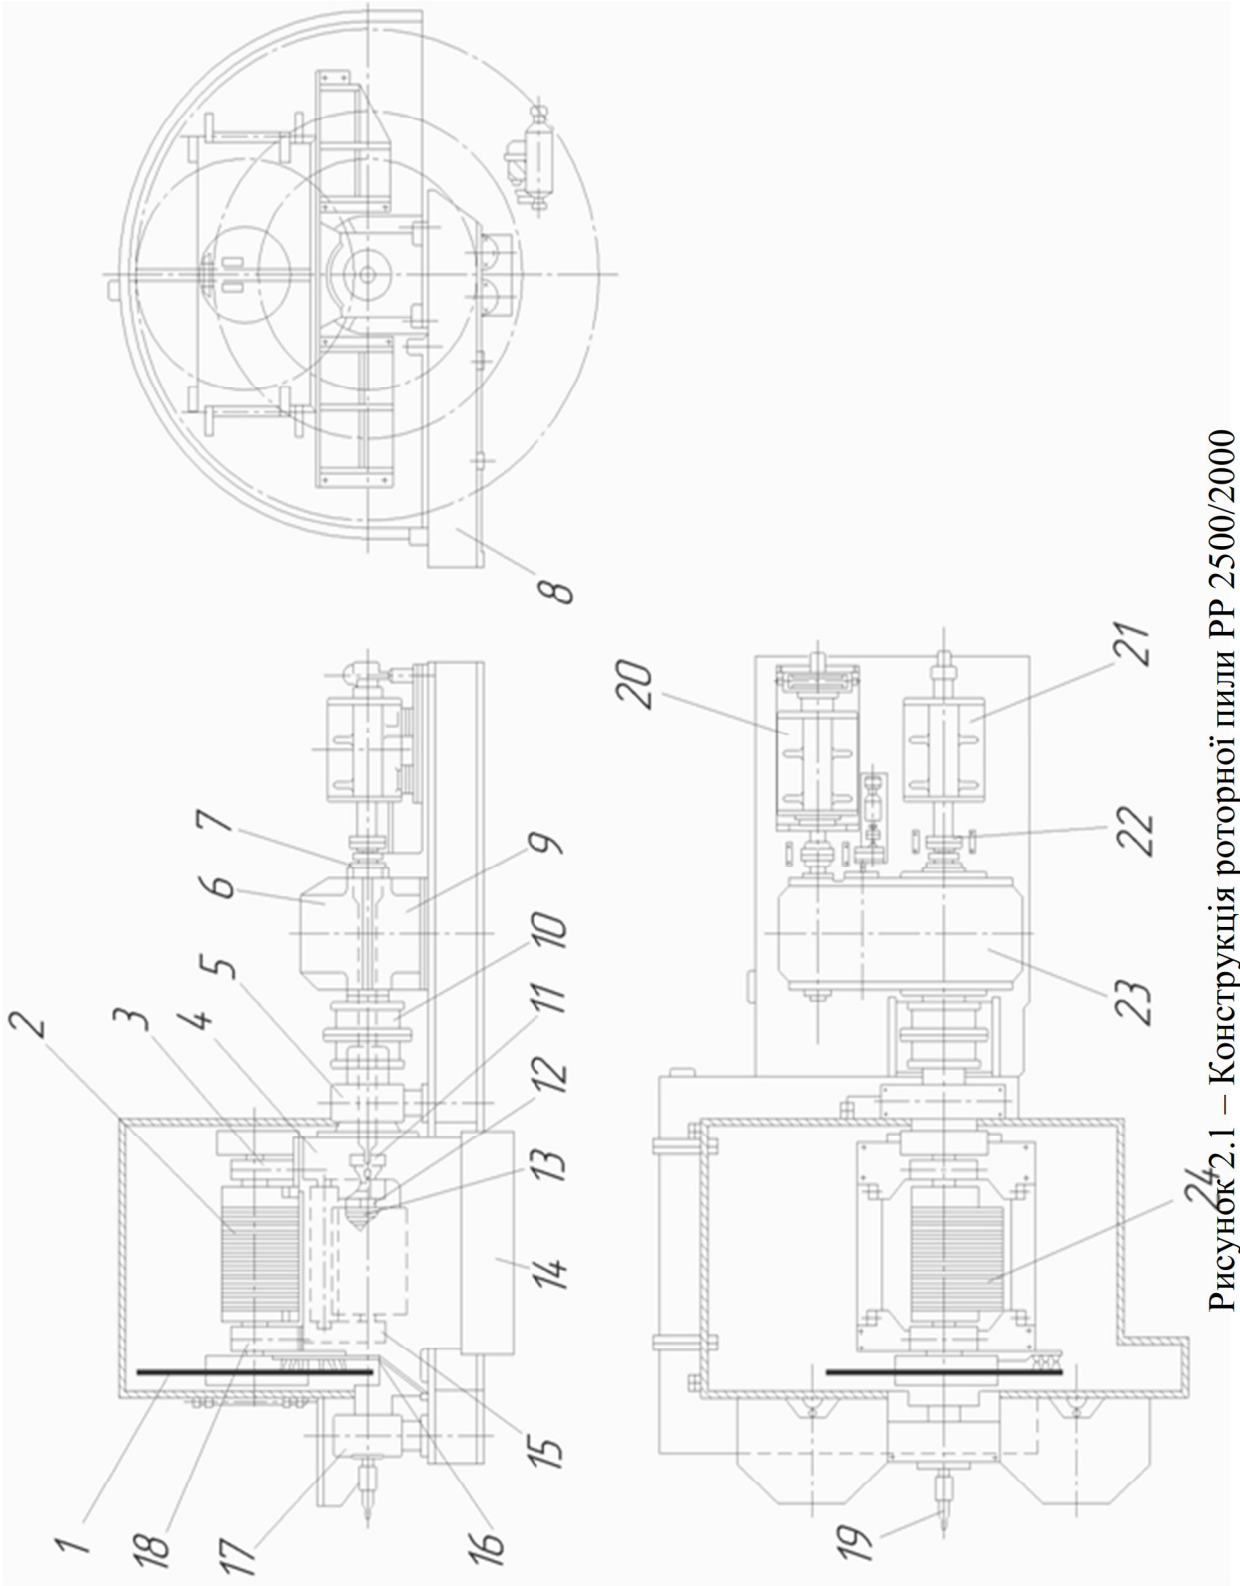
Конструкція роторної пили РР 2500/2000
